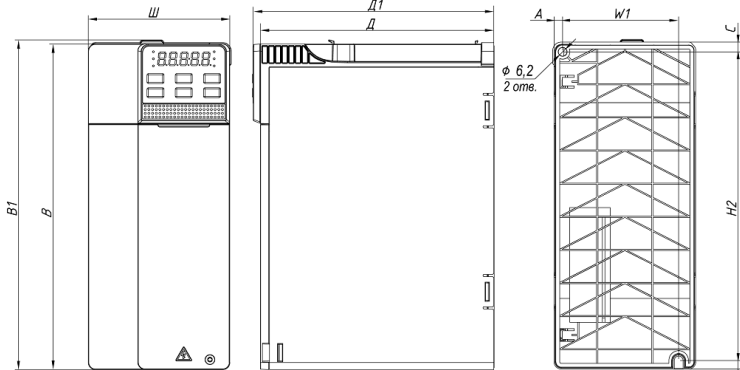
Габаритные и присоединительные размеры (типоразмер 3)
